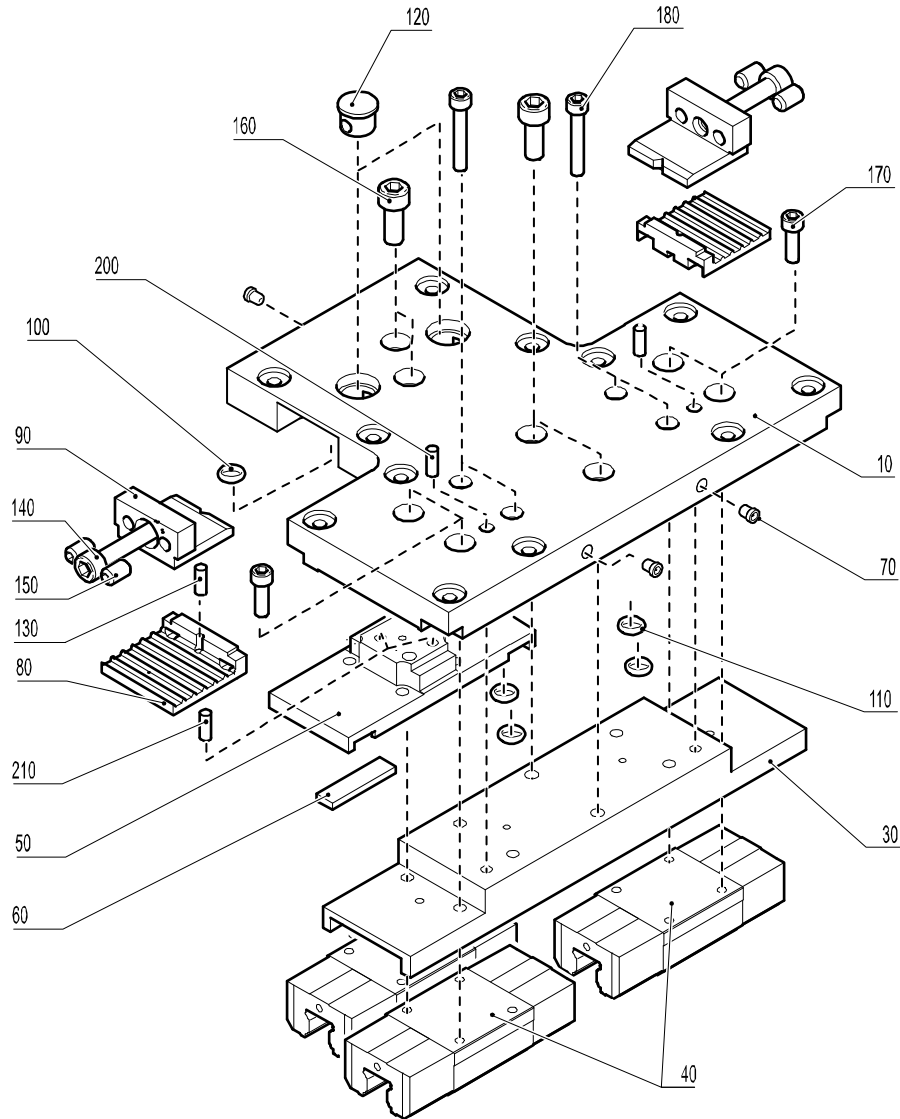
Modul 160/15C, Schlitten komplett, Explosionszeichnung
